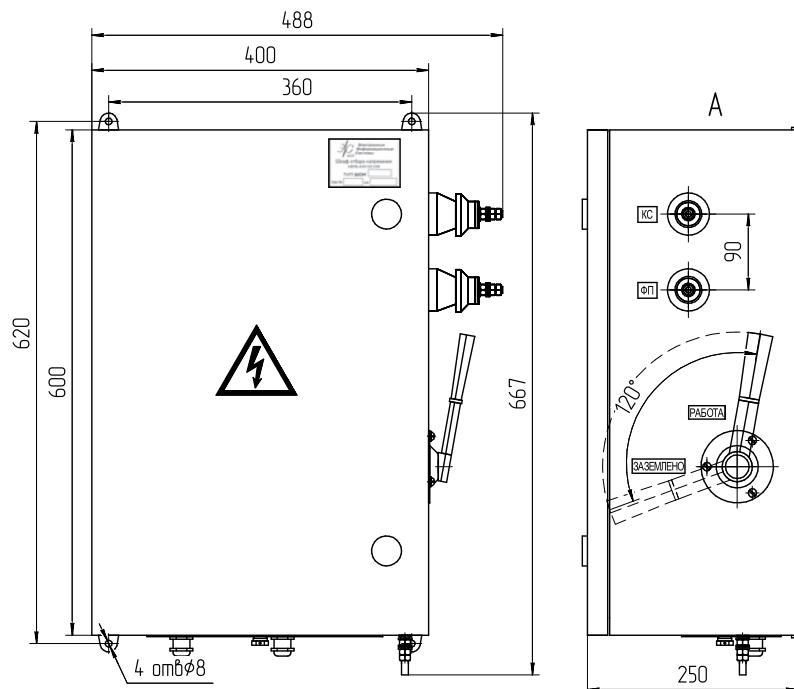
Габаритно-присоединительный чертеж ШОН-303П.
